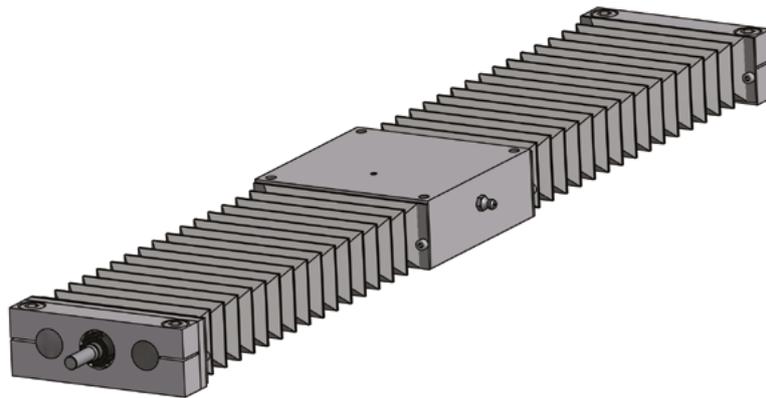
AXLB\_T Kugelbuchsenschisch mit Trapezgewindetrieb
